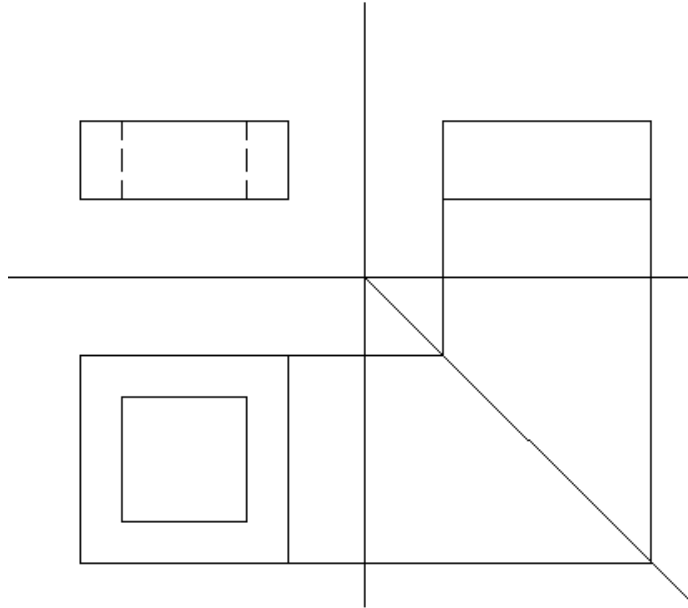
Temel boyutların yatay düzleme taşınması
